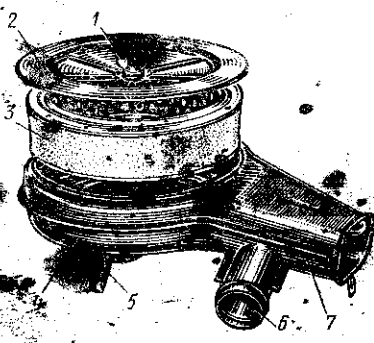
Воздушный фильтр карбюратора К-126Н: 1 — барашковая шпилька; 2 — крышка корпуса; 3 — фильтрующий элемент; 4 — корпус; 5 — патрубок системы вентиляции картера; 6 — патрубок для подсоединения шланга подвода подогретого воздуха; 7 — входной патрубок корпуса
